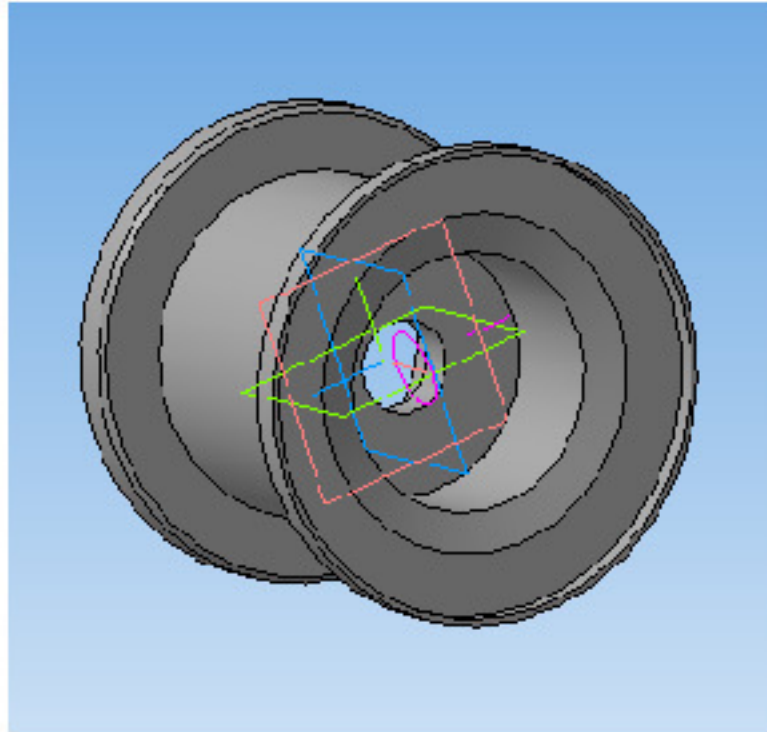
Визначення маси заготовки при литті в оболнкові форми
